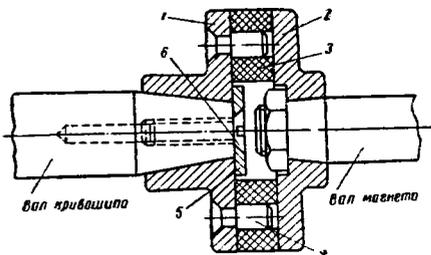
Соединительная муфта привода магнето: 1—фланец на валу двигателя; 2—фланец на валу магнето; 3—упругое кольцо (прорезиненный ремень); 4—штырь; 5—шайба; 6—винт.
